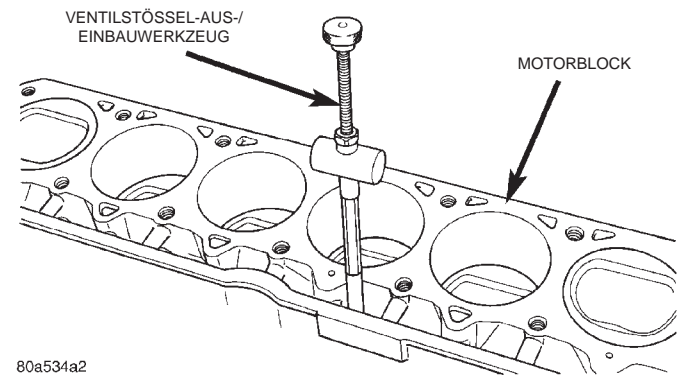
Ausbau-/Einbaugerät für Ventilstößel
